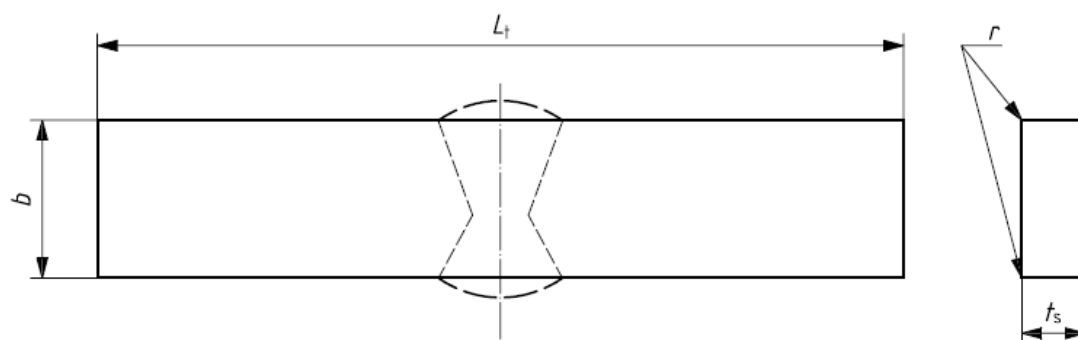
Éprouvette de pliage transversal envers sur soudure bout à bout (TRBB)
